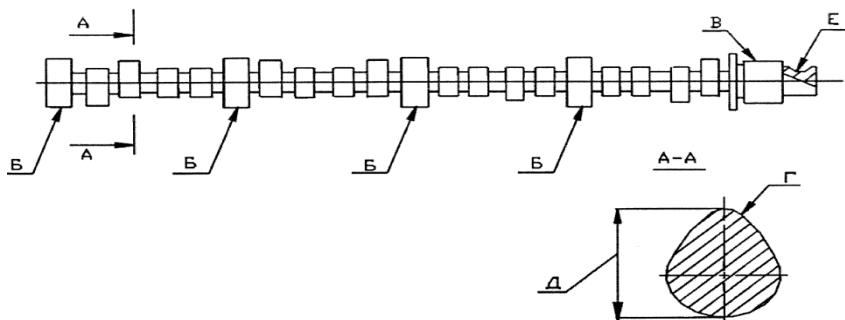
Распределительный вал двигателя КамАЗ-740
